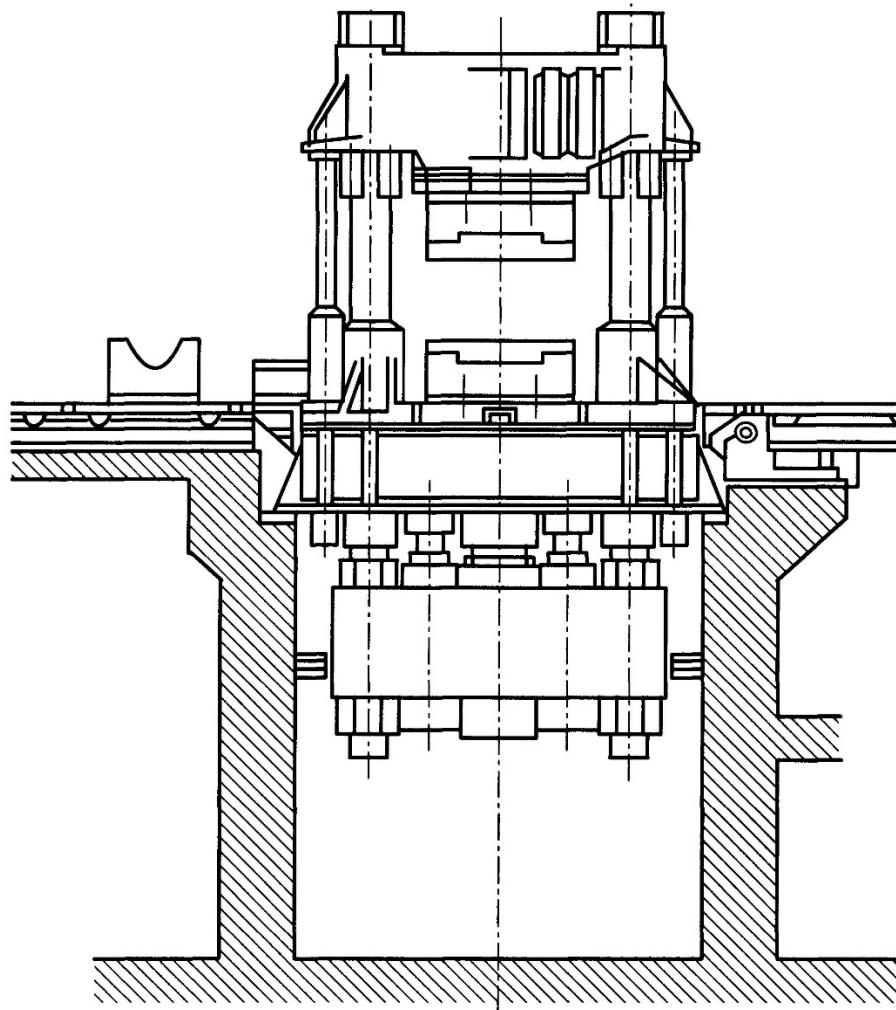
Конструктивна схема куваленого пресу зусиллям 12,5 МН з нижнім розташуванням робочих циліндрів
